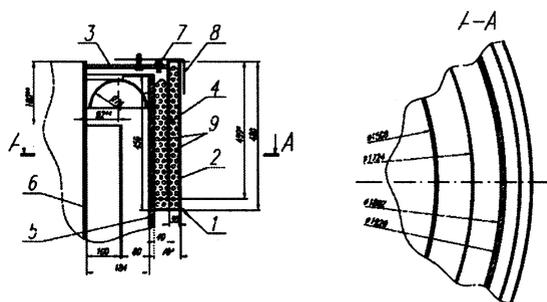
Схема компенсатора радиационного рекуператора: 1 — кольцо; 2 — обечайка; 3 — кольцо; 4 — оболочка; 5 — корпус вагранки; 6 — тепловоспринимающий корпус рекуператора; 7 — пробка; 8 — защитная крышка; 9 — песок
